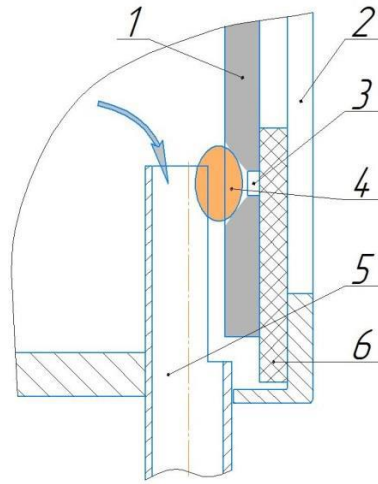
Схема забірного пристрою. 1 – висівний диск; 2 – корпус; 3 – отвір дозуючого елемента; 4 – насіння; 5 – трубка забірного пристрою; 6 – прокладка.
